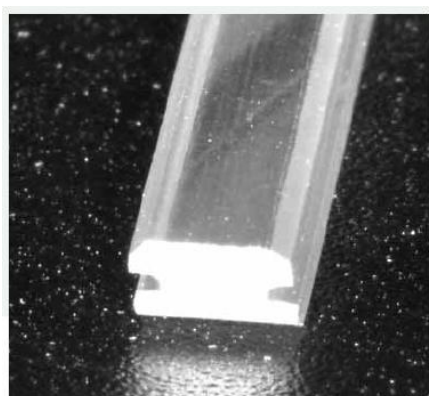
В процессе подготовки к фрезеровке брекетов, кристаллической сапфировой заготовке придается форма.
